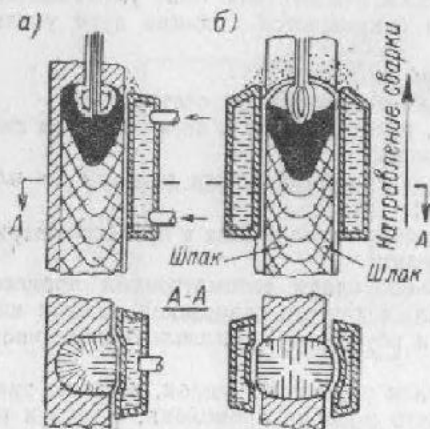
Схема дуговой автоматической сварки под флюсом с принудительным формированием шва: а — шов с несквозным проваром; б — шов со сквозным проваром.
